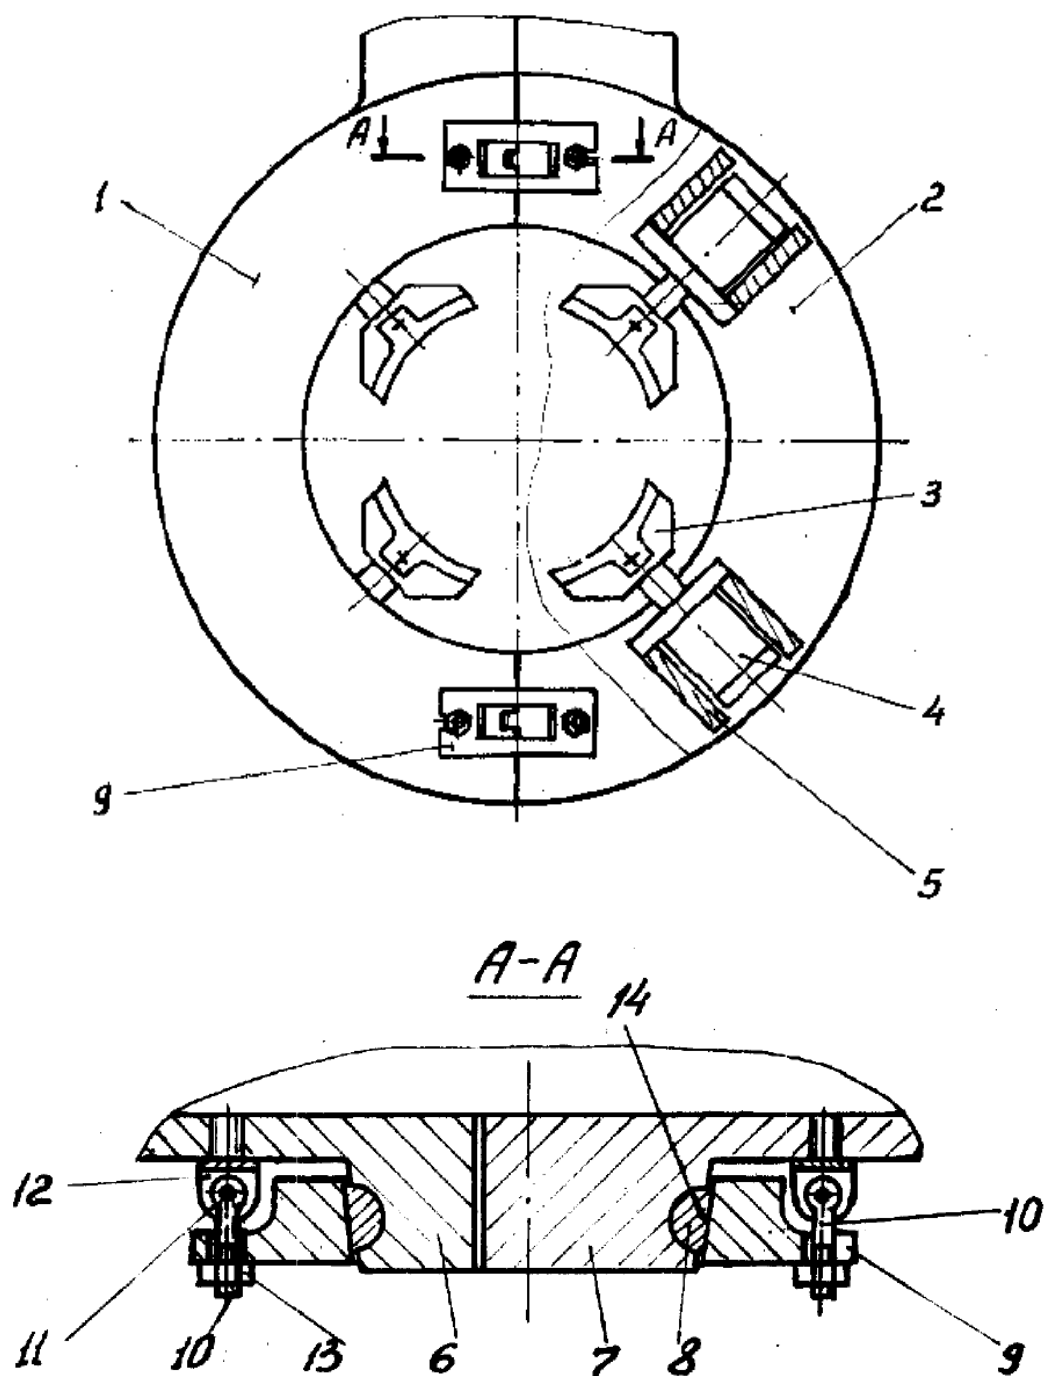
Приспособление для сборки под сварку толстостенных труб
